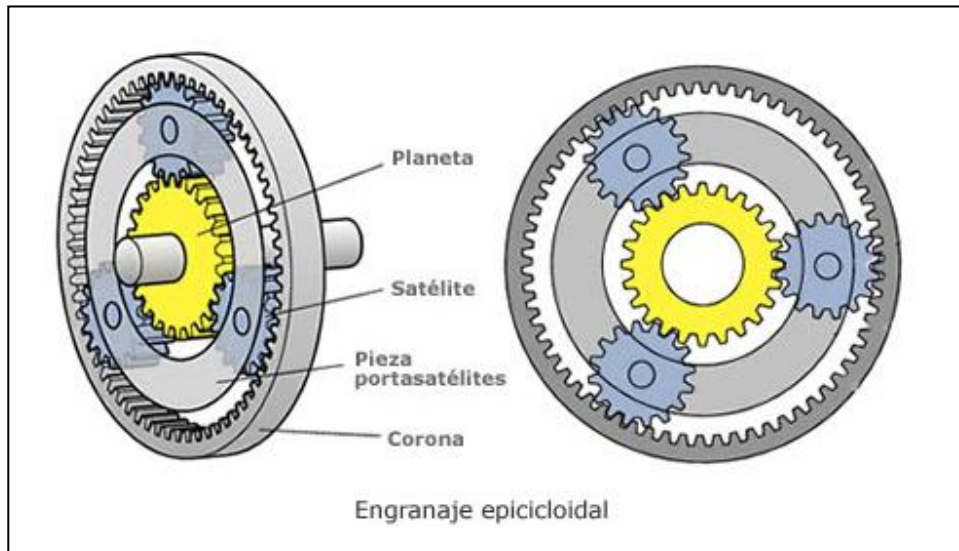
Engranajes Epicicloidial o Engranaje Planetario⁷⁴
